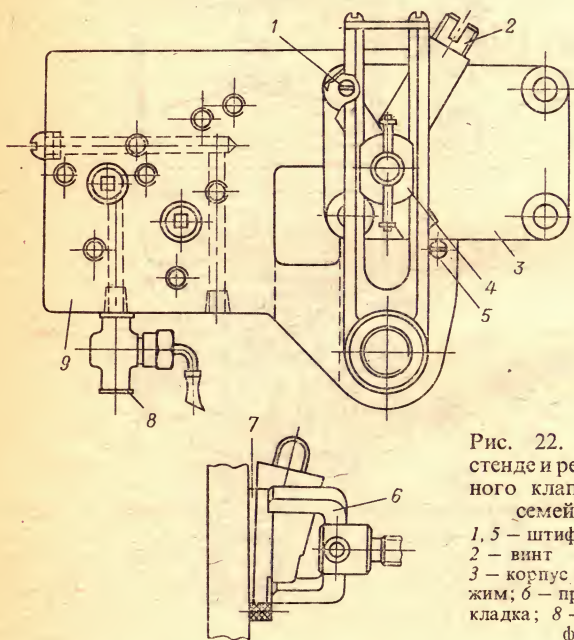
Установка на стенде и регулировка сливного клапана двигателей семейства СМД:
